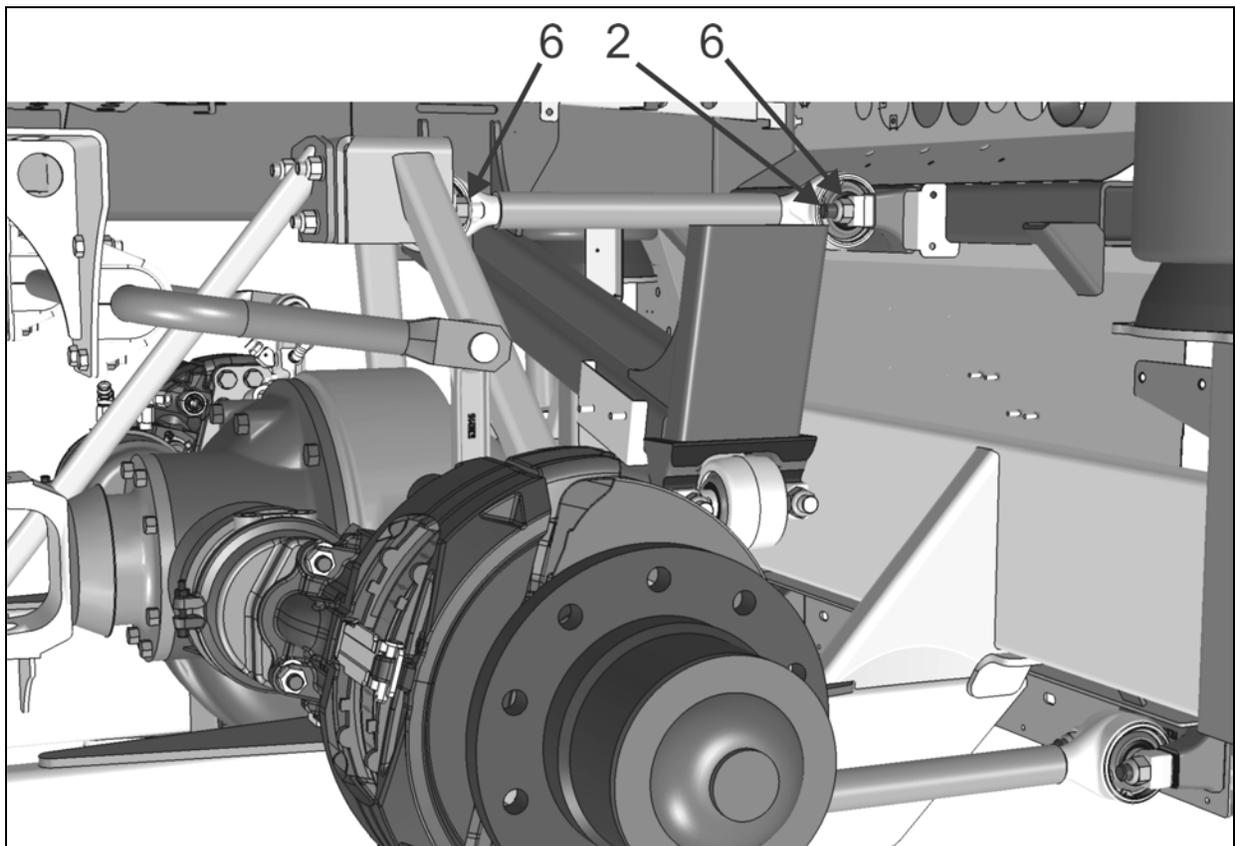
COUPLES DE SERRAGE – ESSIEU MOTEUR, HAUT
